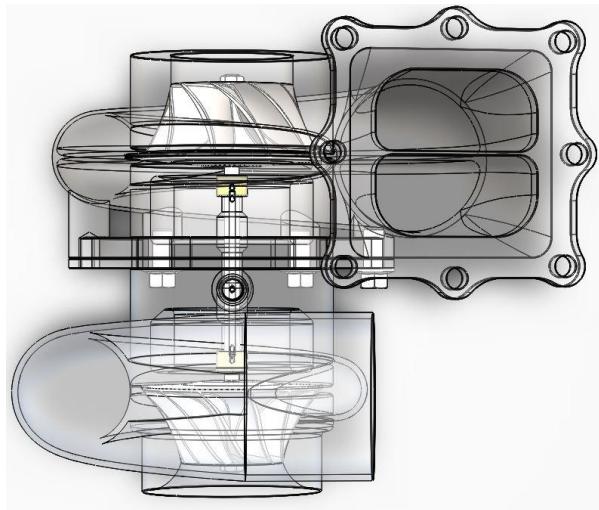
Трехмерный чертеж ТКР-7С-6М с подробной прорисовкой его размеров
